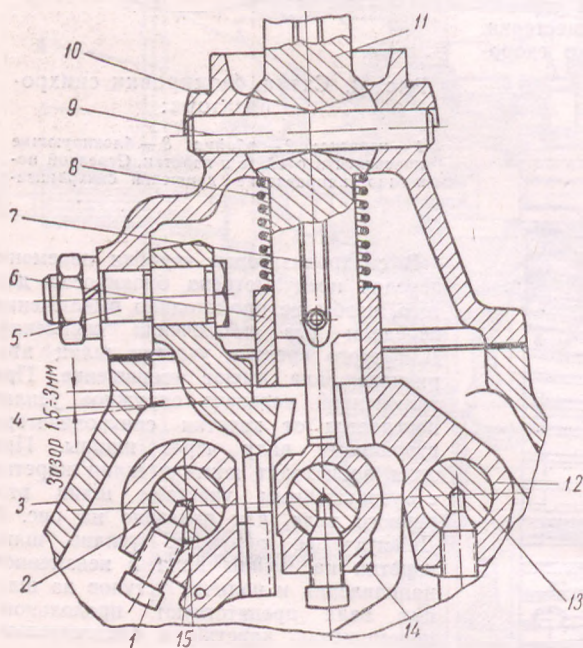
Предохранительное устройство для предупреждения случайного включения 1-й передачи и передачи заднего хода:
